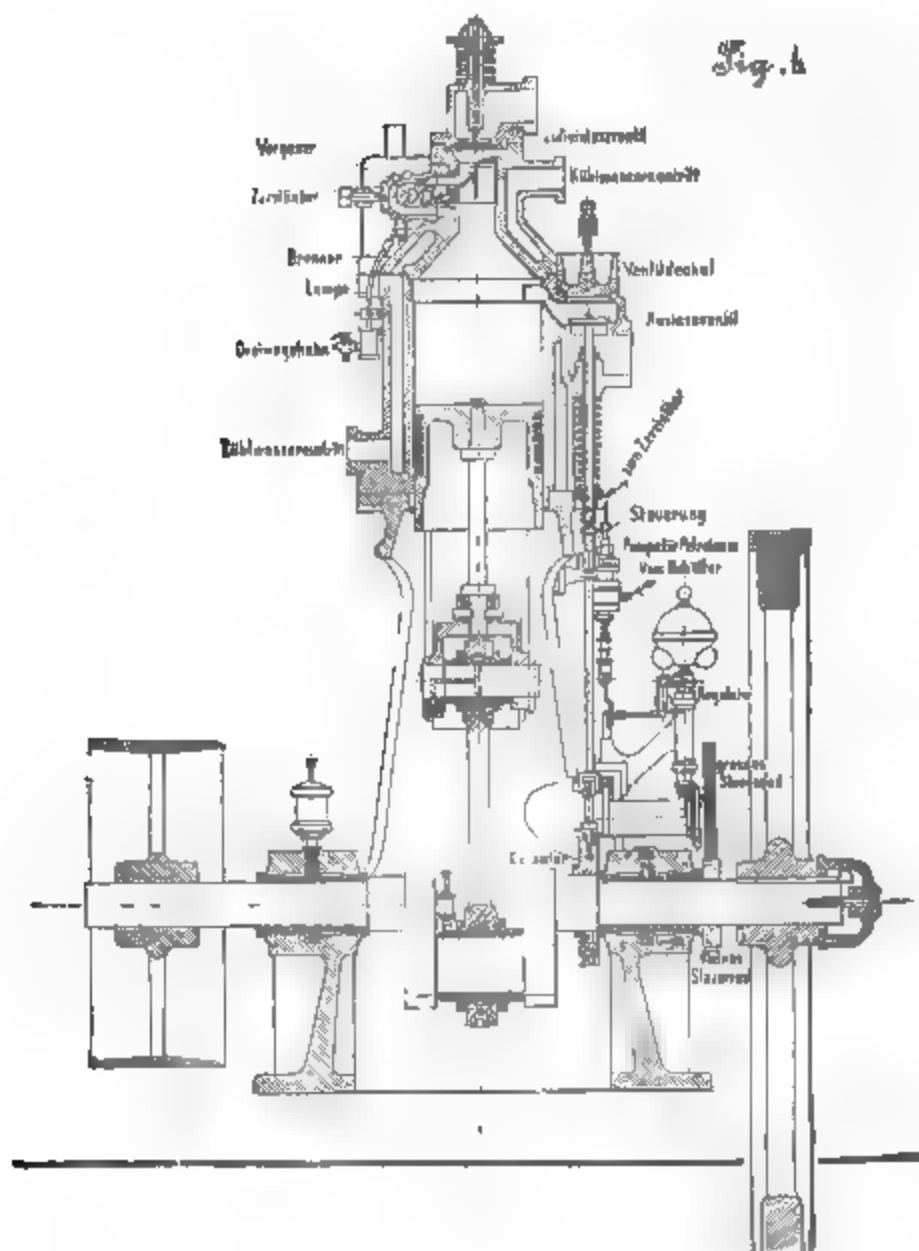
Petroleummotor von Grob & Comp., Leipzig.
